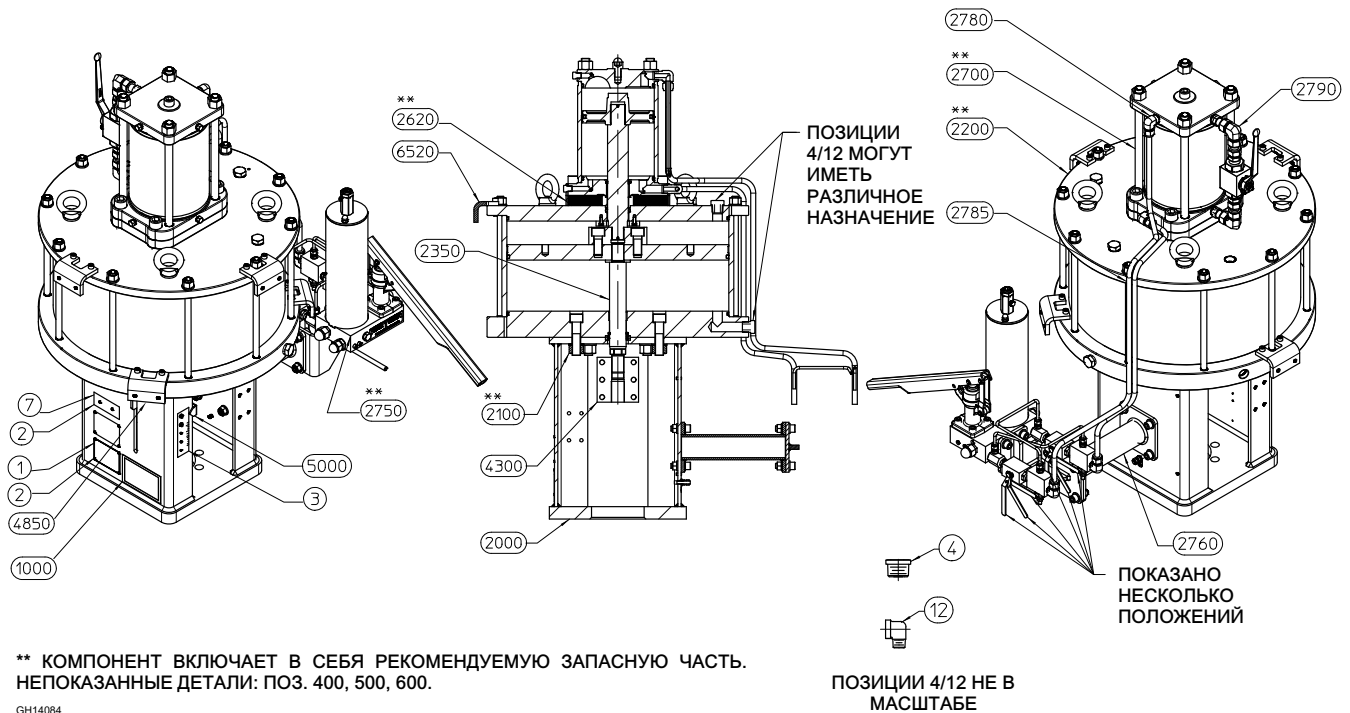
Беспружинный привод Fisher 785С в сборе без ручной коррекции
